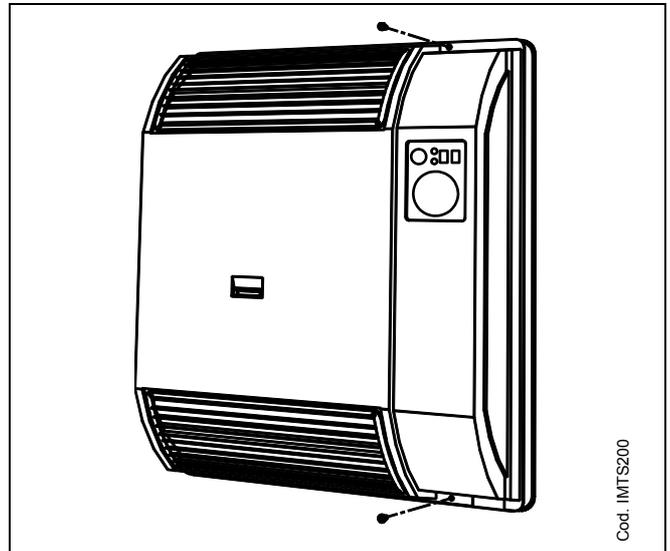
GEHÄUSESCHRAUBEN 3001 U. 3002
